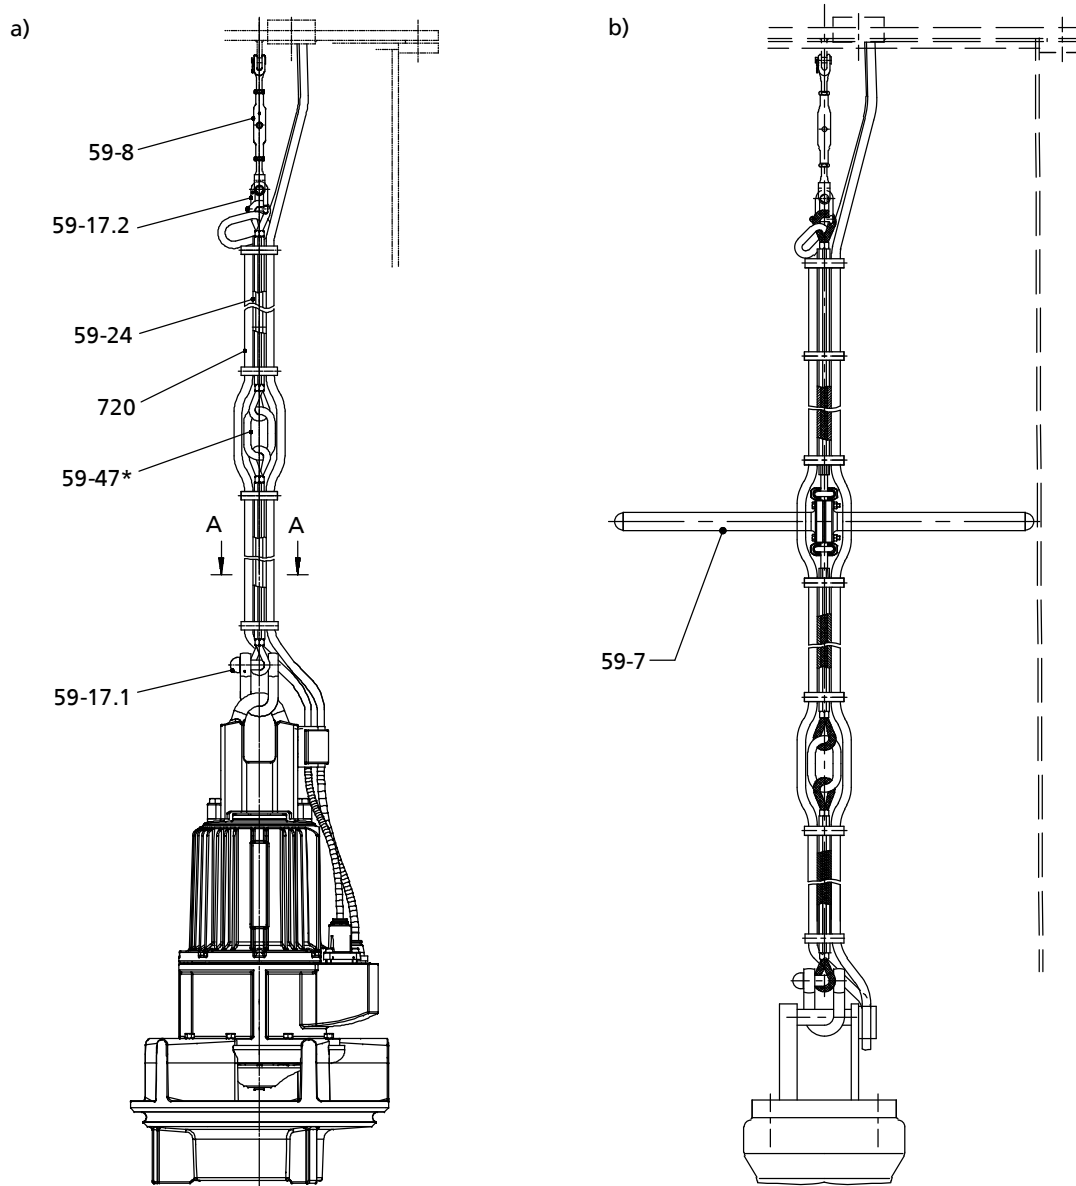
a) Pumpenaggregat mit Tragseil und Spannschloss im Rohrschacht b) Pumpenaggregat mit Tragseil und Spannschloss im Rohrschacht für große Einbautiefen mit Stützkörper
